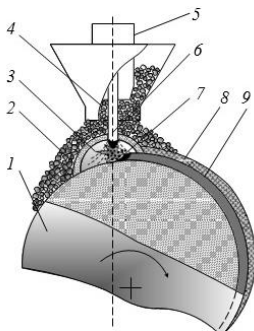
Схема наплавлення під шаром флюсу:
